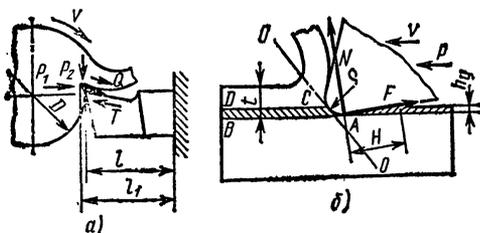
Схемы образования нароста на резае (а) и наклепа обработанной поверхности заготовки (б)
